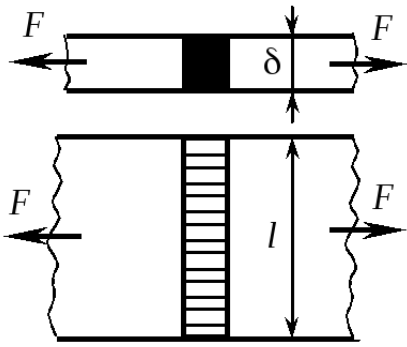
Розрахункова схема стикового зварного з'єднання
